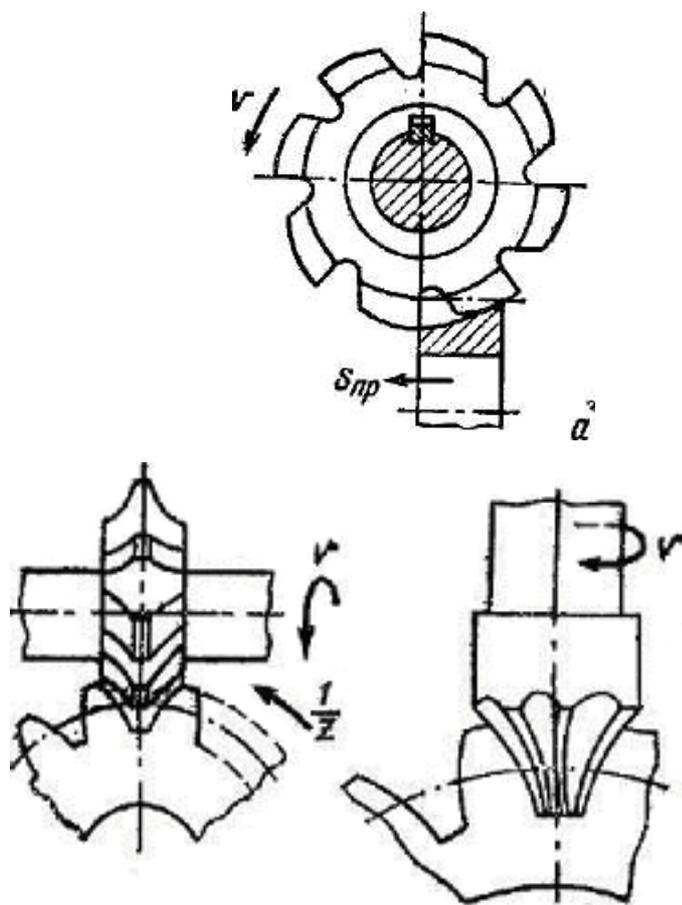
Схема фрезерования зубьев зубчатых колес методом копирования
